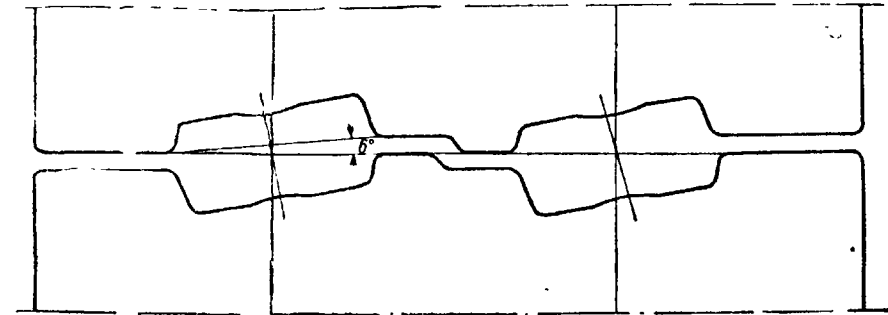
Диагональная калибровка валков непрерывного заготовочного стана
